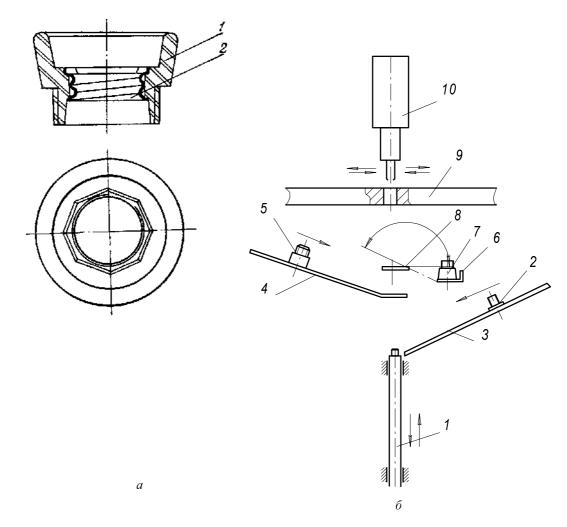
Складання металевої гільзи з керамічним корпусом: а — конструкція вузла; б — технологічний процес складання
